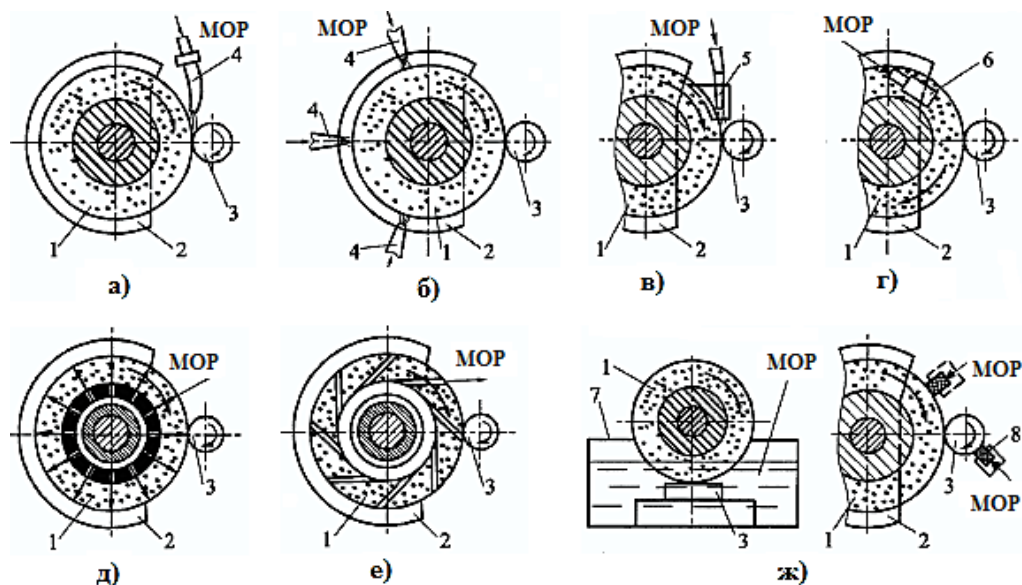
Схеми основних способів подачі МОР при шліфуванні: 1 - шліфувальний круг; 2 - кожух; 3 - шліфувана заготовка; 4 - сопло; 5 - насадка; 6 - торцева насадка; 7 - ємкість з МОР; 8 - м'який пористий матеріал, просочений мастилом
